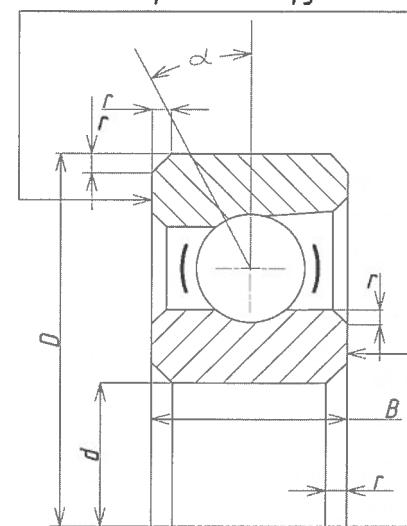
Конструкция подшипников шариковых однорядных радиально-упорных, тип 6000, 36000, 46000 (ГОСТ 831-75)
